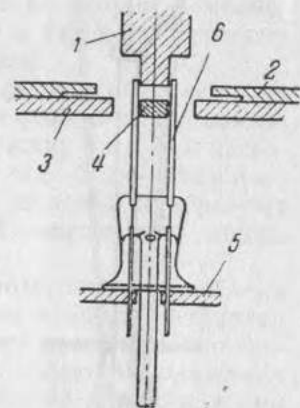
Приспособление для обрубки и формовки электродов.
